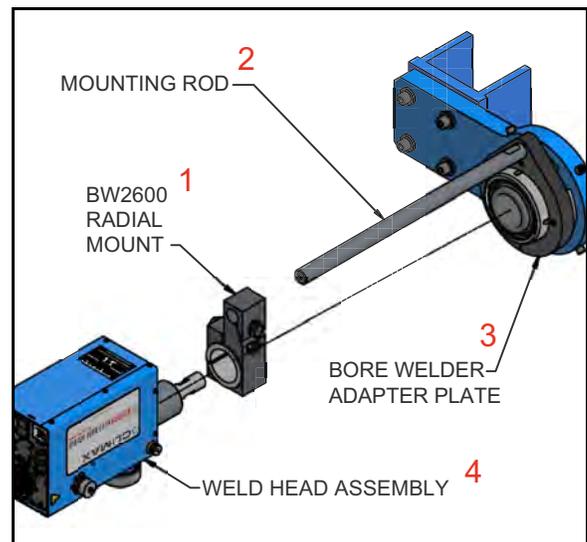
BW2600 COMPOSANTS DE L'ENSEMBLE
